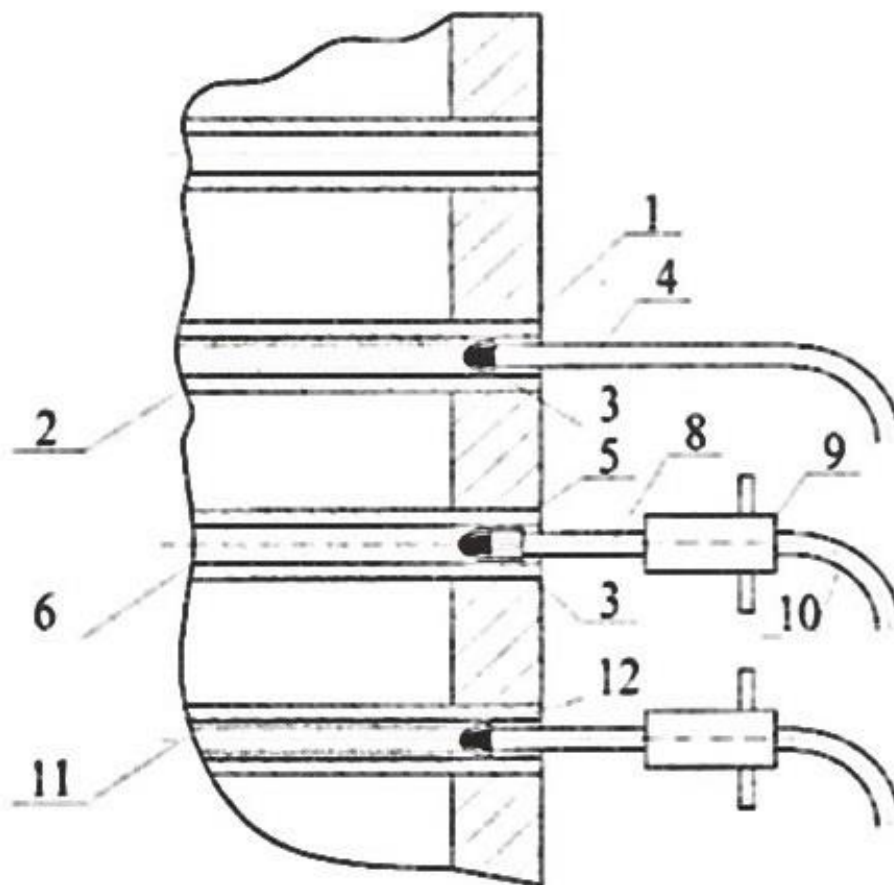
Схема очистки трубок теплообменников зубчатыми коронками:
